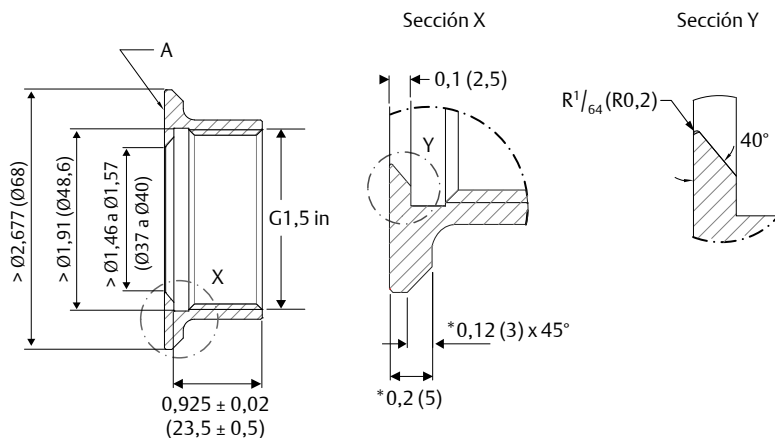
Sello de metal a metal con tope soldado
